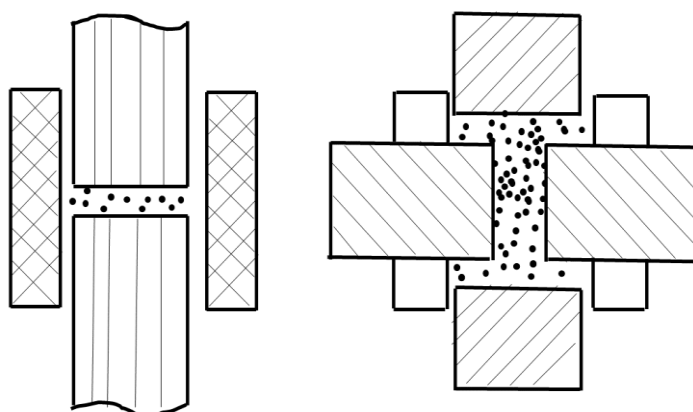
Возможные схемы диффузионной сварки деталей с применением порошковых промежуточных прослоек: а- сварка стержней встык; б-сварка листов встык.
